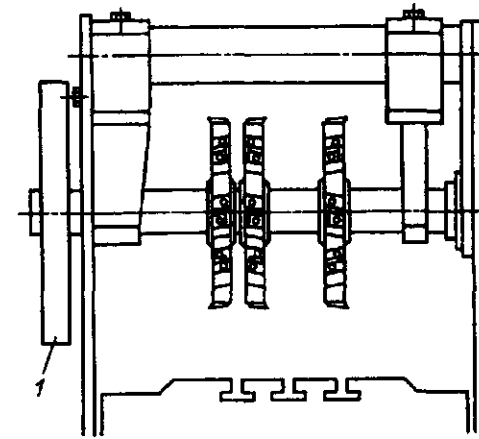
Набор дисковых фрез для обработки пазов: 1 — маховик
